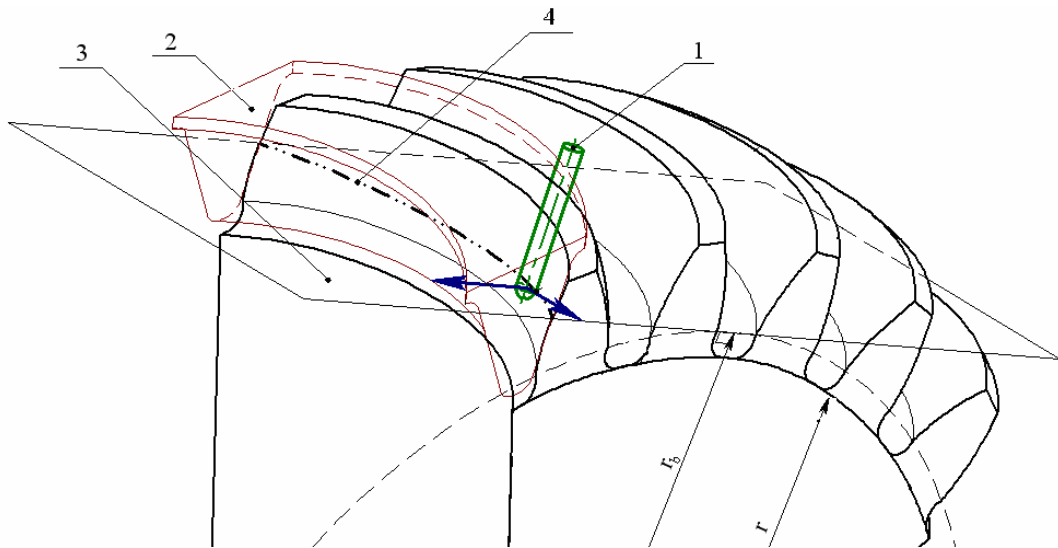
Верстатне зачеплення пальцевої фрези з арочним зубом:
